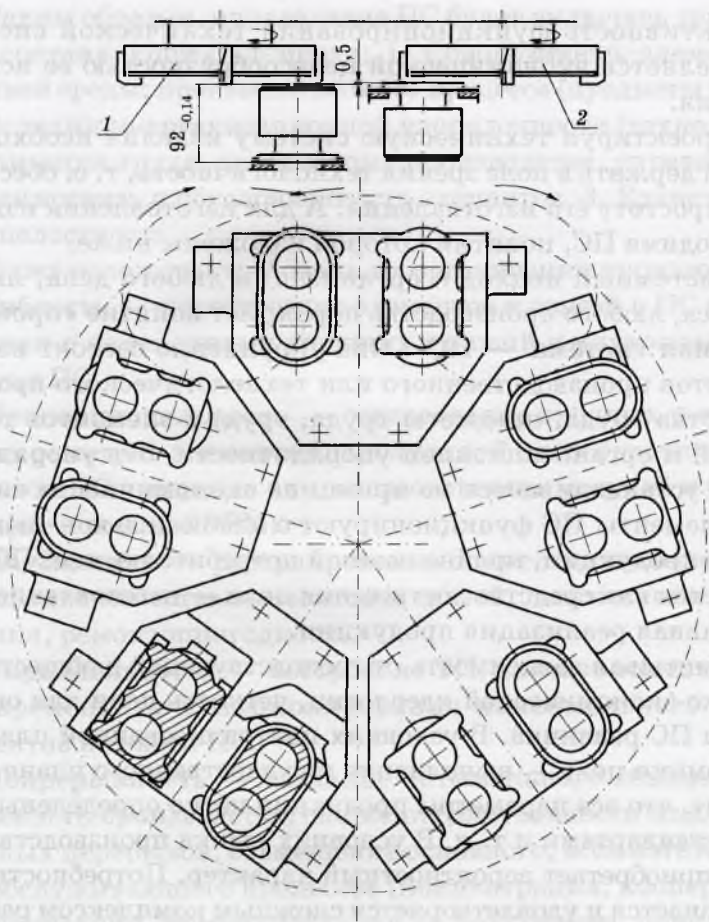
Схема операции фрезерования заготовки с двух сторон на карусельном полуавтомате: фрезы черновой (1) и чистовой (2) обработки заготовок
